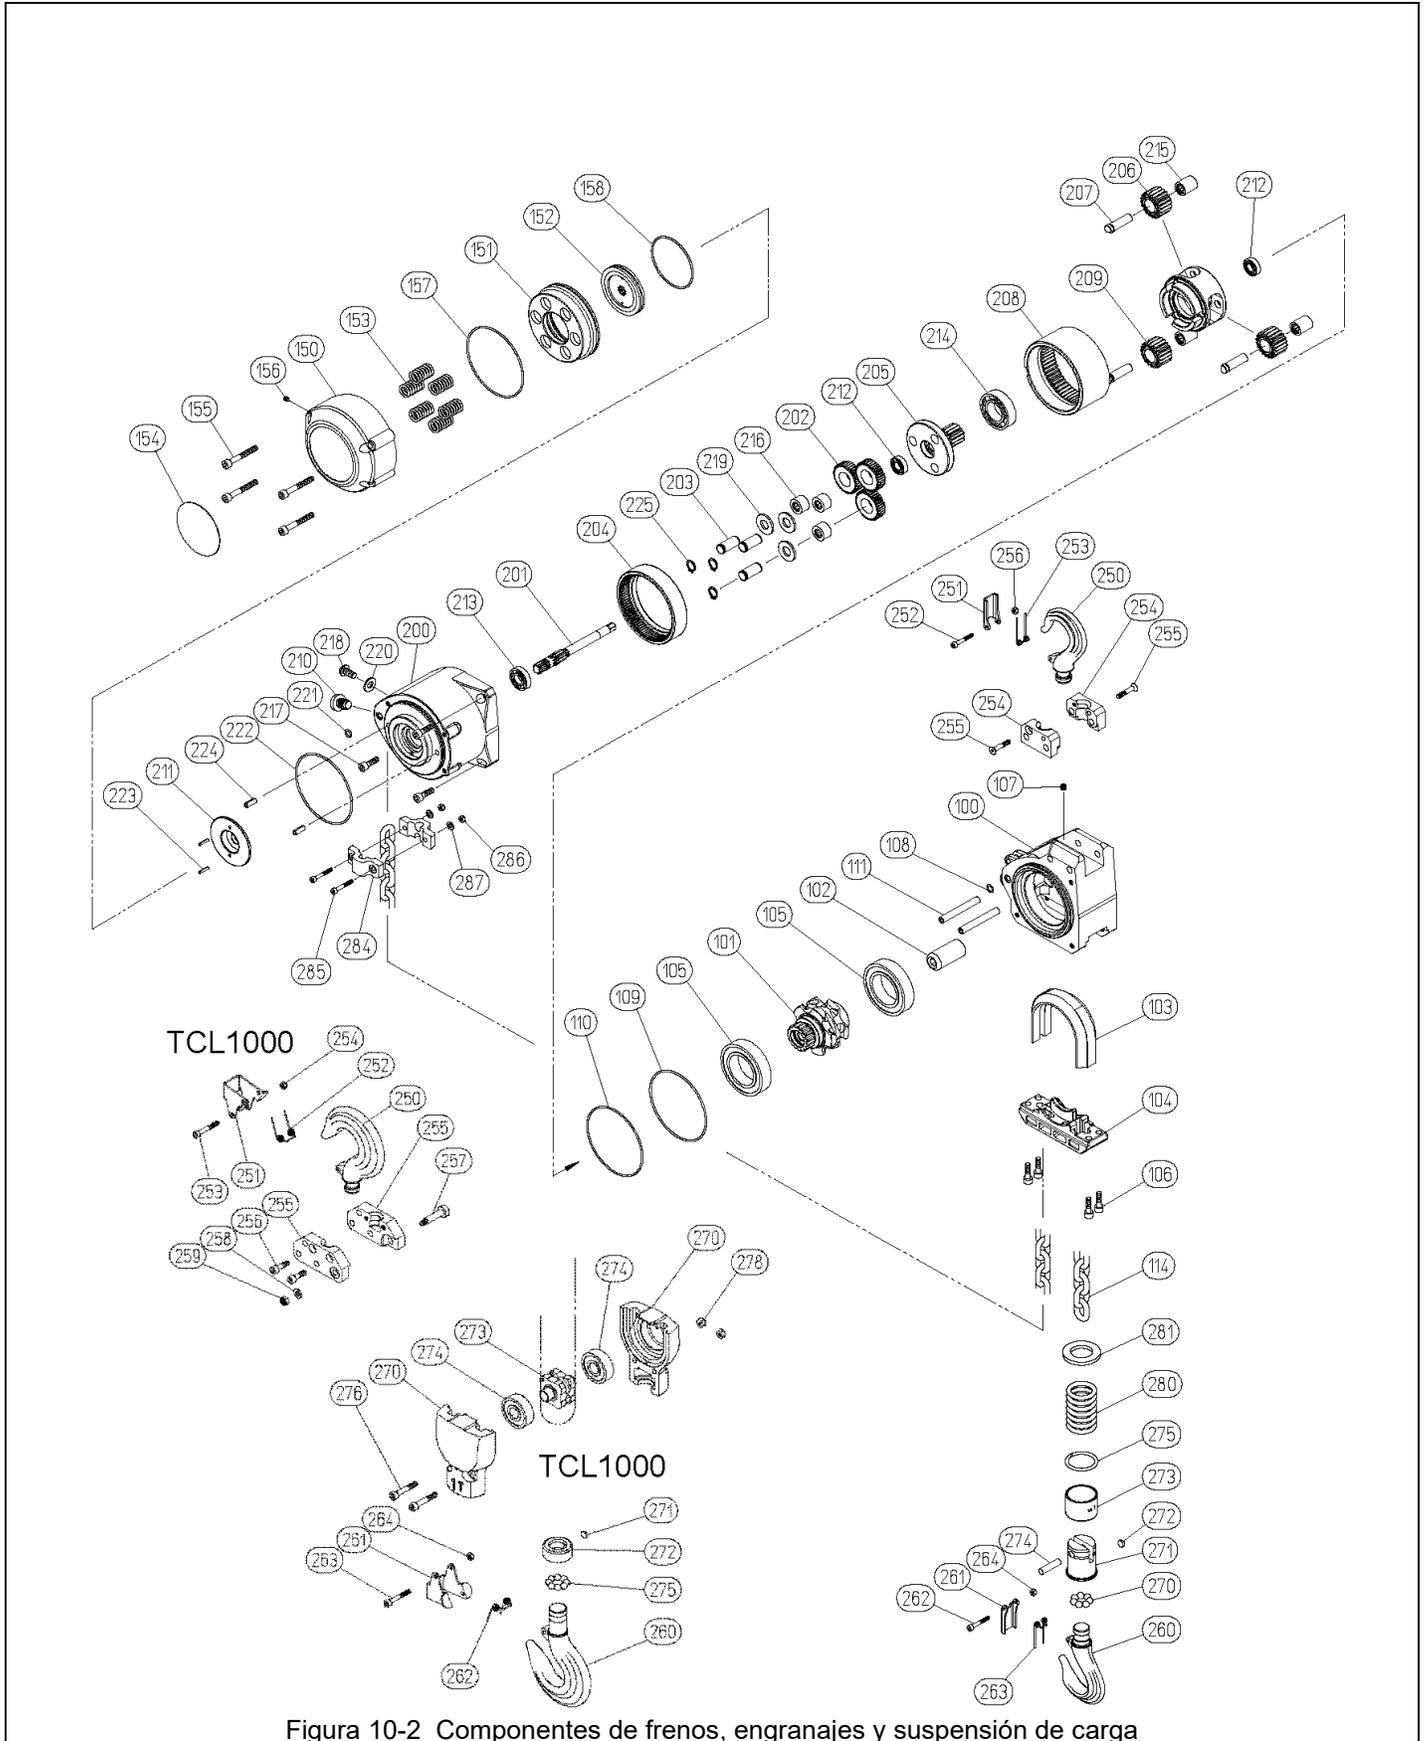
Componentes de frenos, engranajes y suspensión de carga
